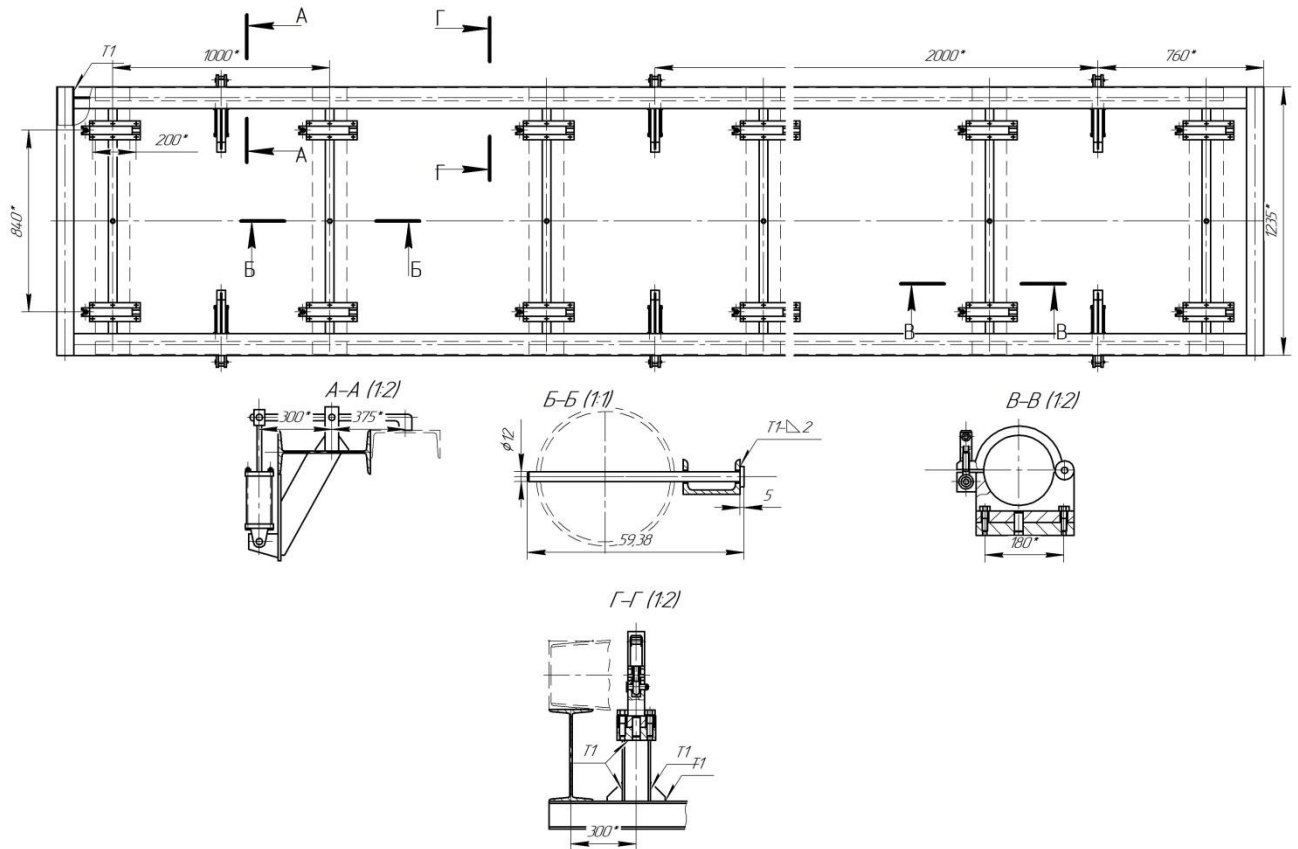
Кондуктор для складання та зварювання основи
